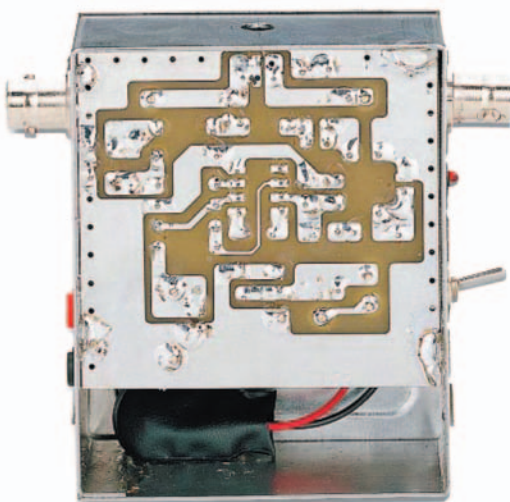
Photo d'un des prototypes de la platine installé dans son boîtier de blindage, côté soudures.
